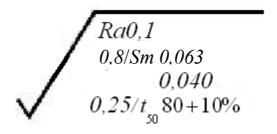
Обозначение шероховатости при двух и более параметрах
